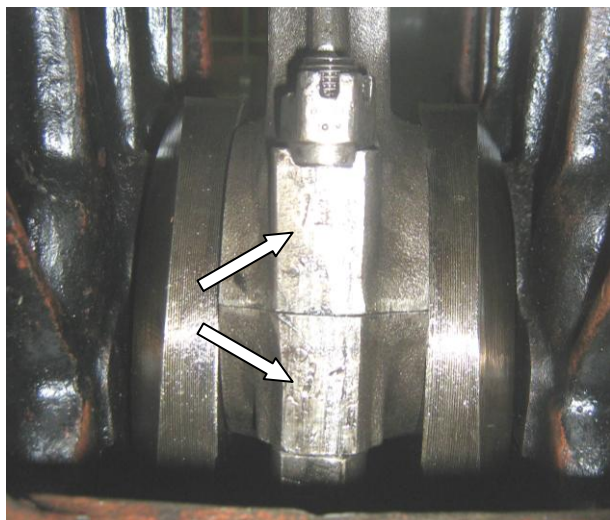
Маркировка крышки и стержня шатуна
